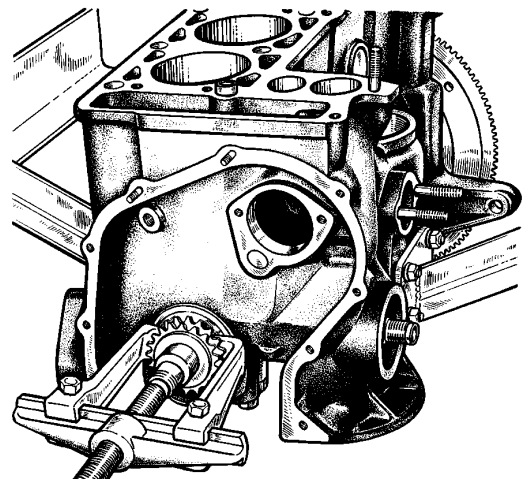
Ausbau des Kurbelwellenrads mit Universalvorrichtung
